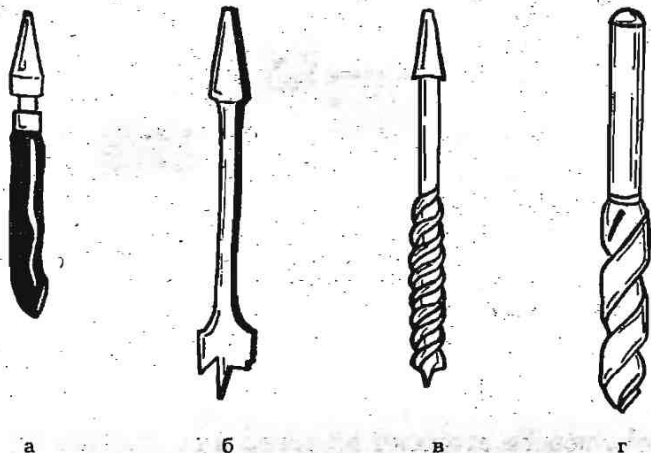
Виды сверл: а — ложечное; б — центровое; в — винтовое; г — спиральное
